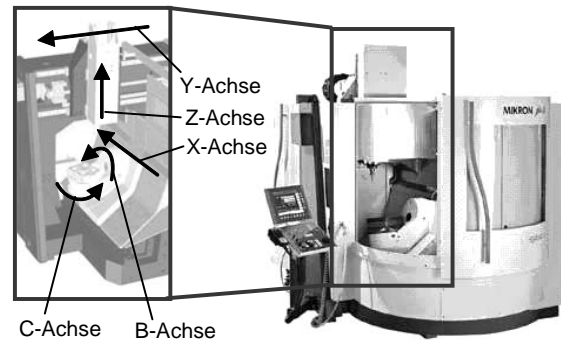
Maschinengrundträger HSM 600 U und dessen Spezifikationen (Mikron AG)
